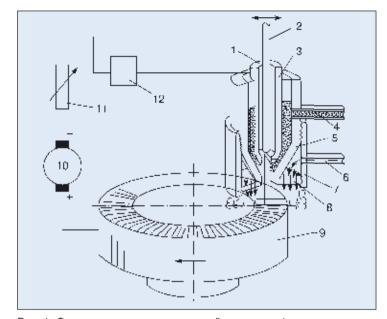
Схема плазменно-порошковой наплавки: 1 — ввод плазмообразующего газа; 2 — вольфрамовый электрод; 3 — стабилизирующее сопло; 4 — ввод транспортирующего газа с присадочным порошком; 5 — фокусирующее сопло; 6 — ввод защитного газа; 7 — защитное сопло; 8 — газовая линза; 9 — наплавляемая деталь; 10 — источник питания дуги; 11 — резистор; 12 — устройство поджига дуги
